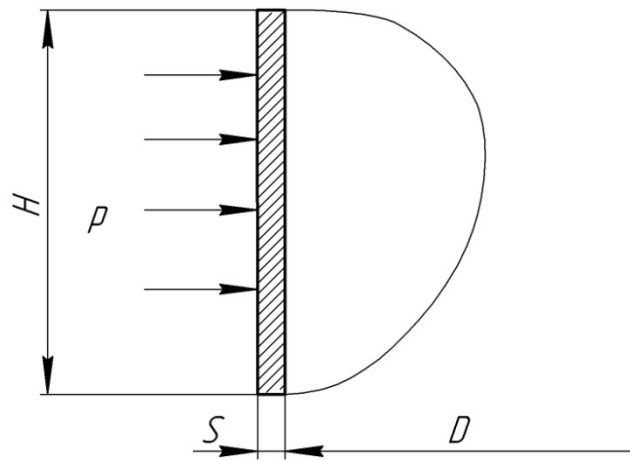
Розрахункова схема для розрахунку товщини стінки циліндричної обичайки, що знаходиться під зовнішнім тиском
